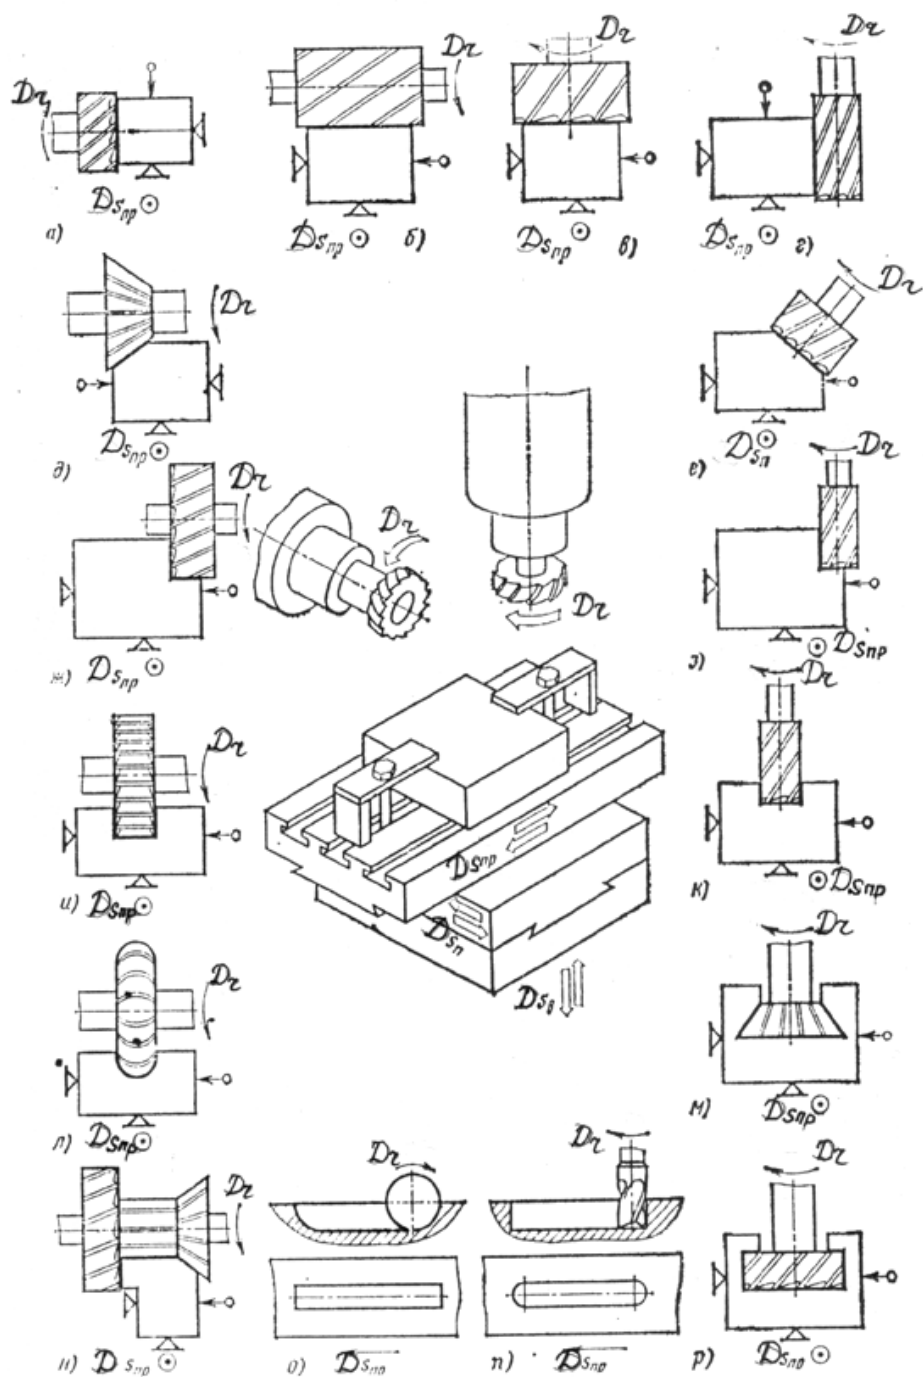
Схемы обработки поверхностей фрезерованием
